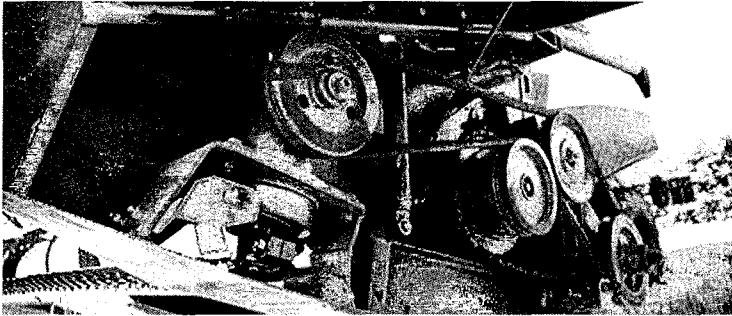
Планетарный привод ножей типа Schumacher
